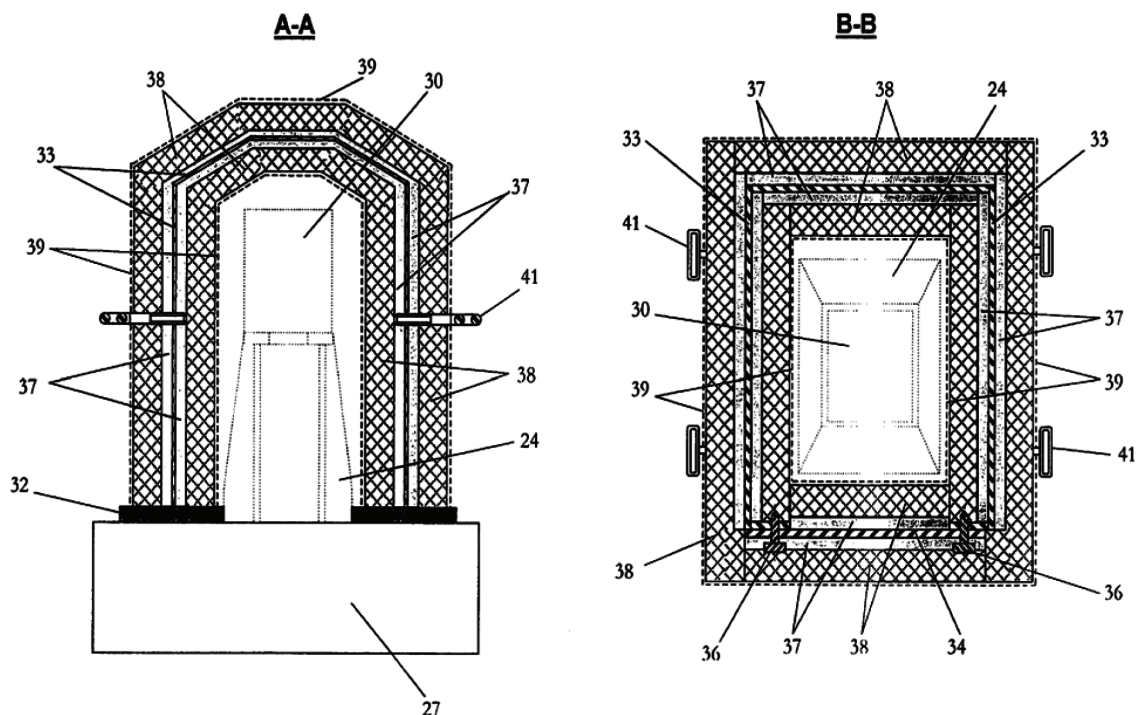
Схема конструкции акустической капсулы корпуса верхнего опорного подшипникового узла (разрезы А-А и В-В):
